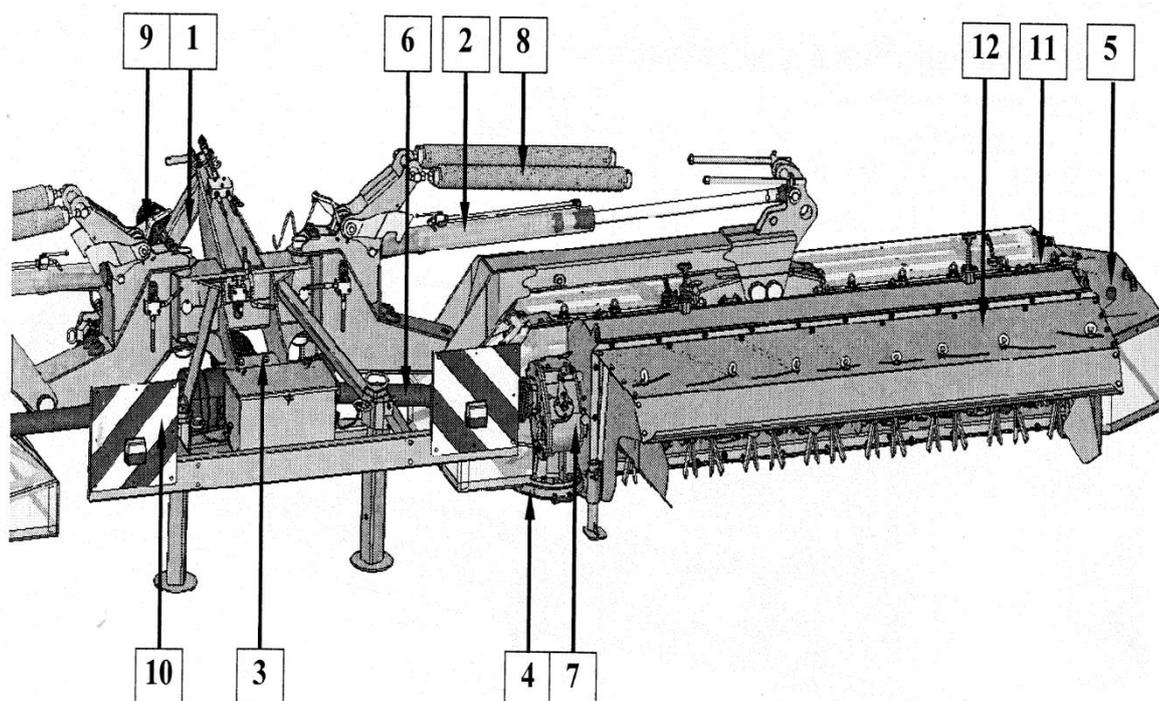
Общий вид косилки дисковой двусторонней со вспушивателем
